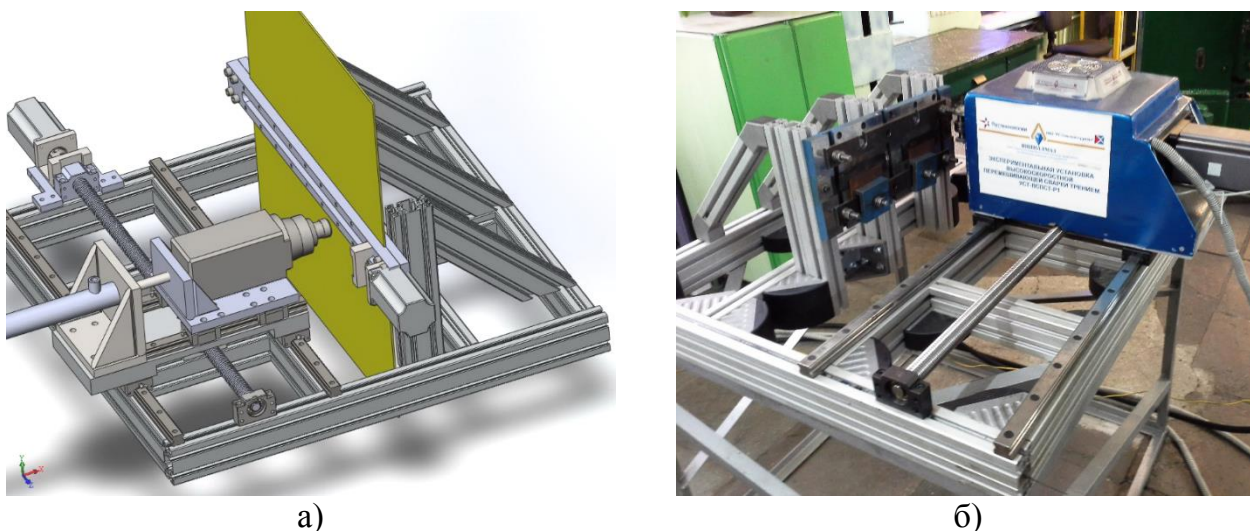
Установка высокоскоростной сварки трением перемешиванием (ВСТП):
